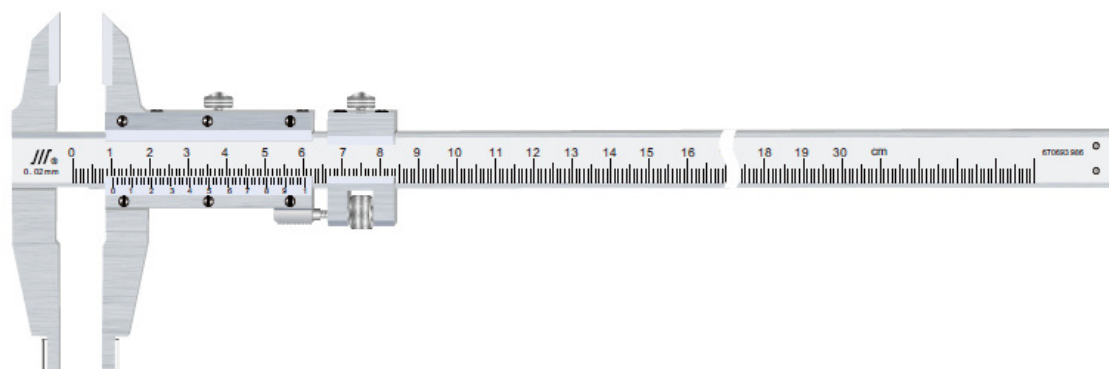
Общий вид штангенциркулей модели ШЦ-II
